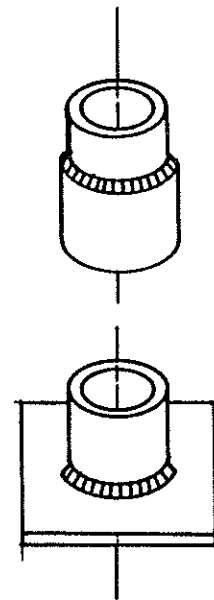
Posiciones de soldadura de Filete para chapas
